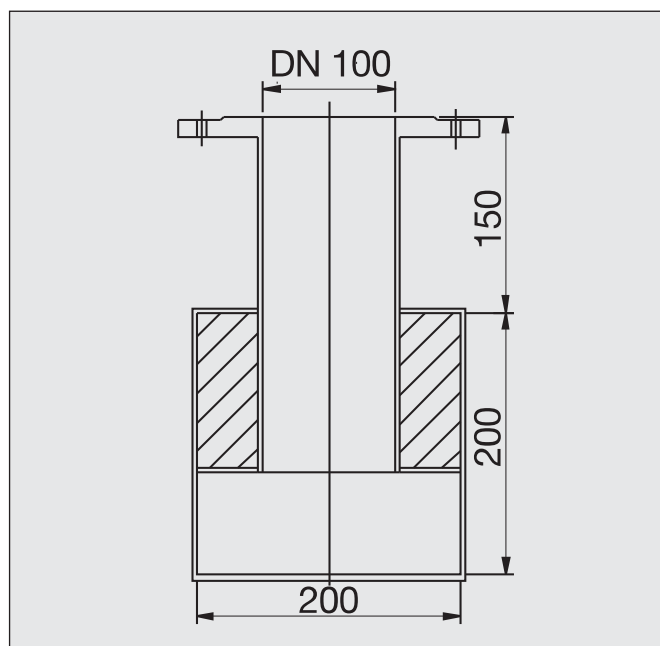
Hrdla přírub v jedné rovině, standardní délky 150mm
